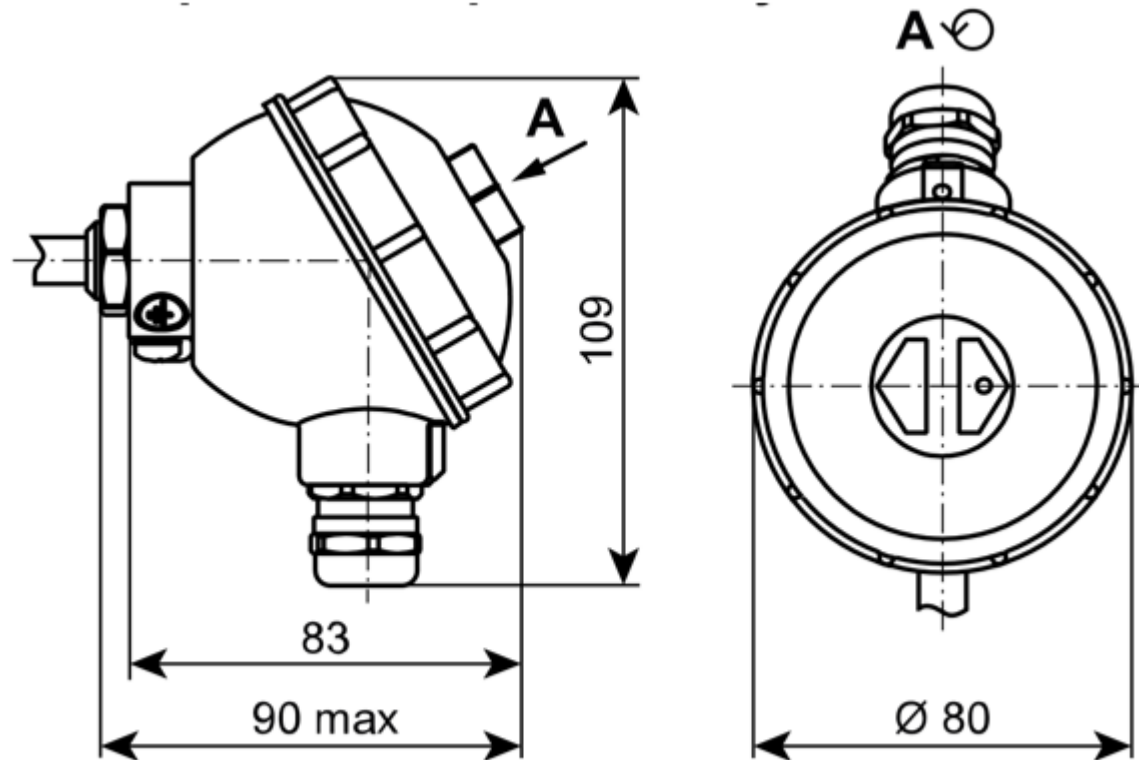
Габаритный чертеж коммутационной головки
